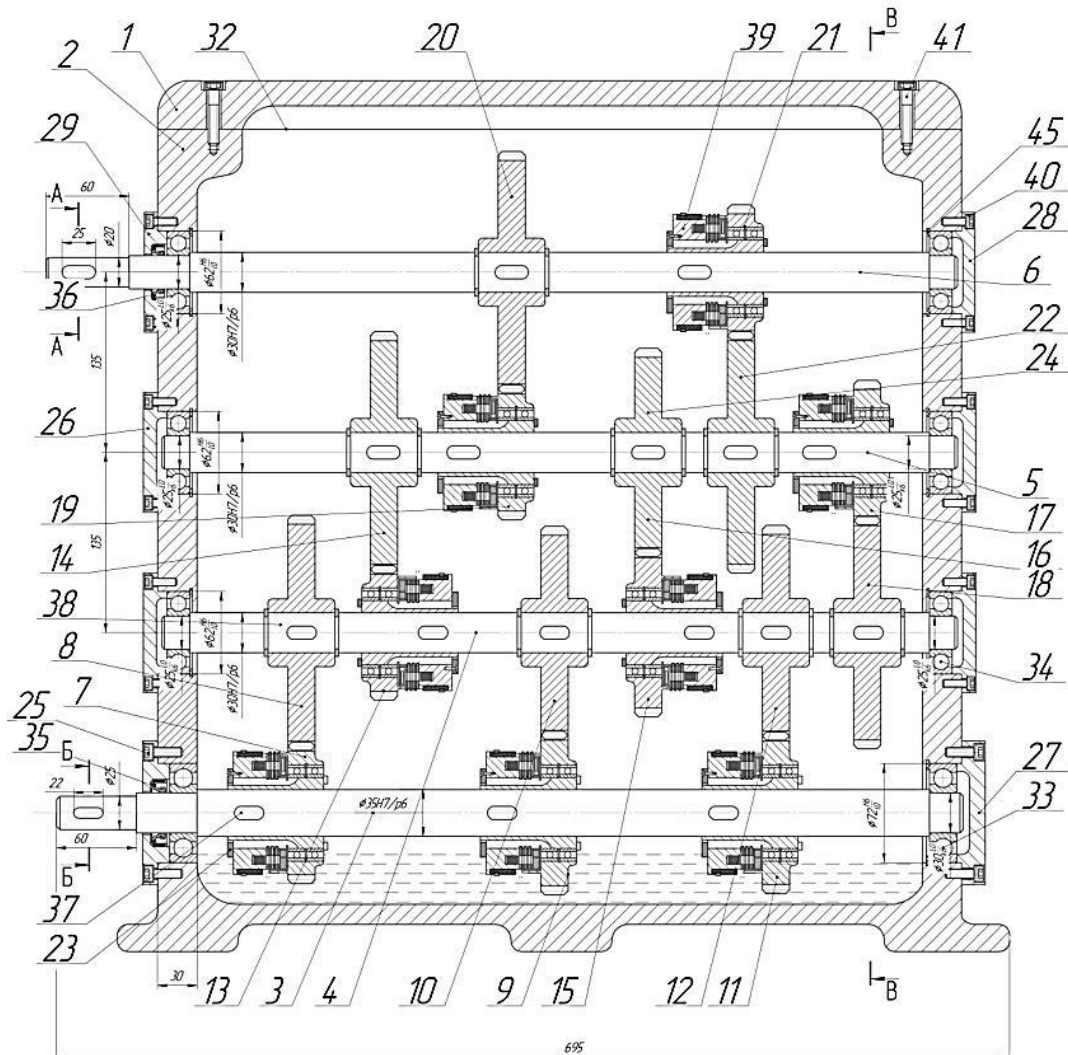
Конструкція розгортки коробки швидкостей модернізованого приводу головного руху
